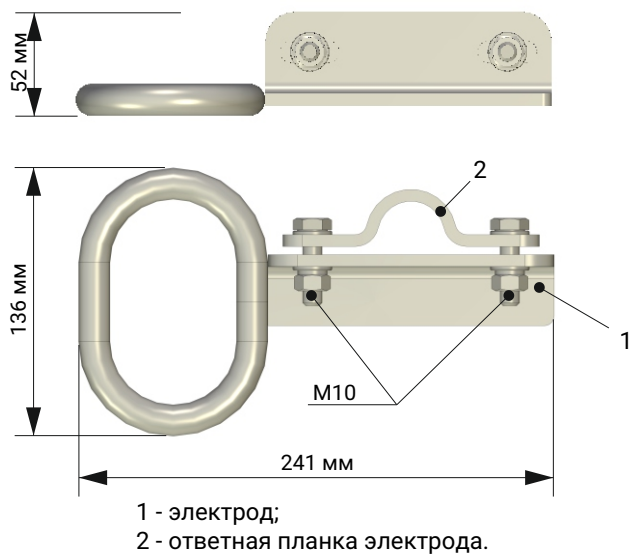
Внешний вид и габаритные размеры электрода на изолятор
